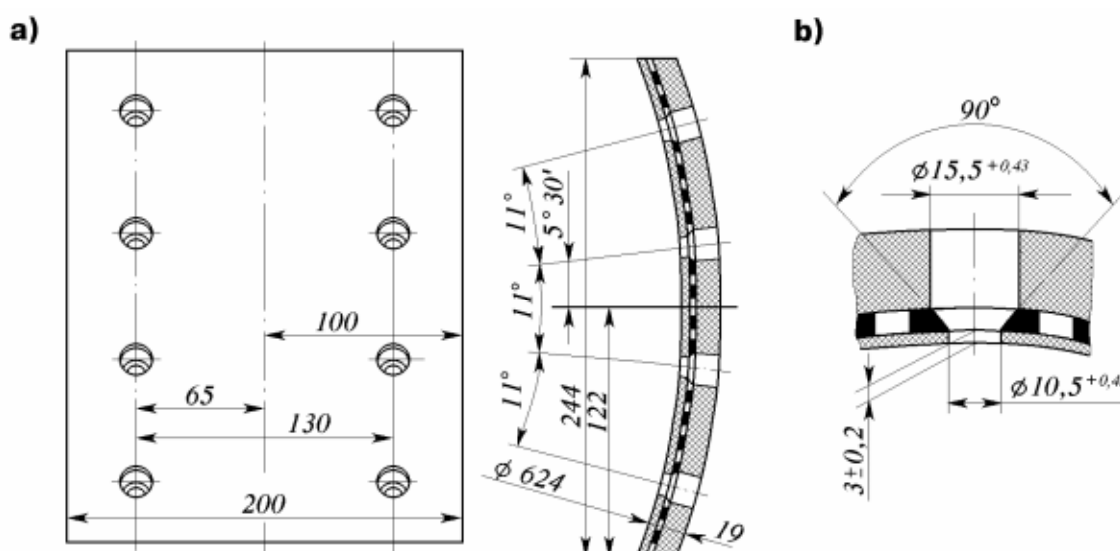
Накладка колодки тормозного механизма (эскизы для обработки):
